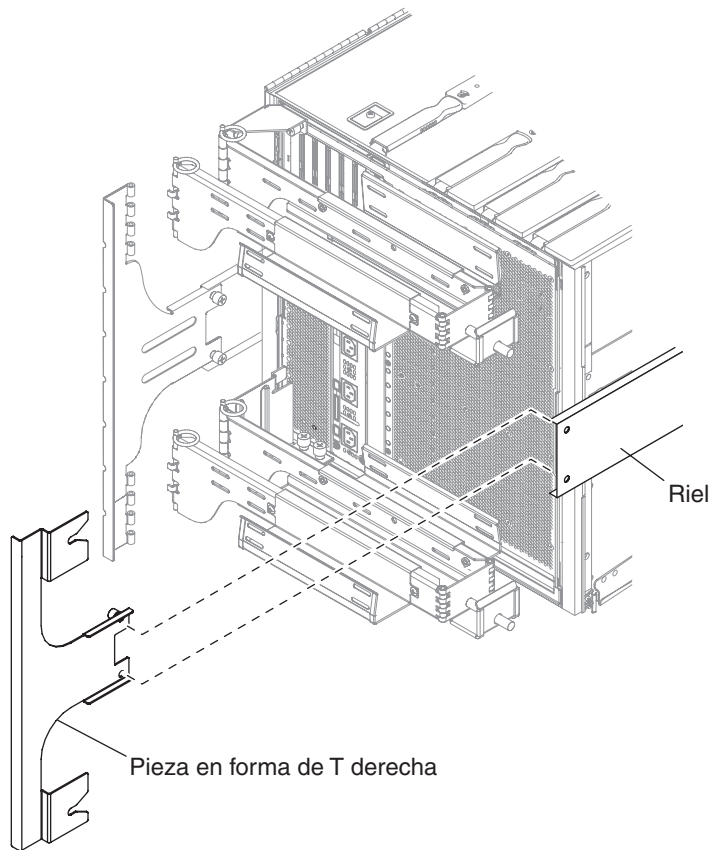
Montaje de la pieza en forma de T derecha
